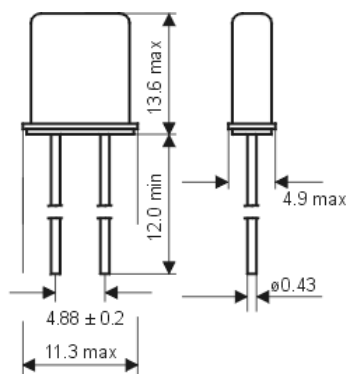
Габаритні розміри кварцового резонатора 4 МГц
